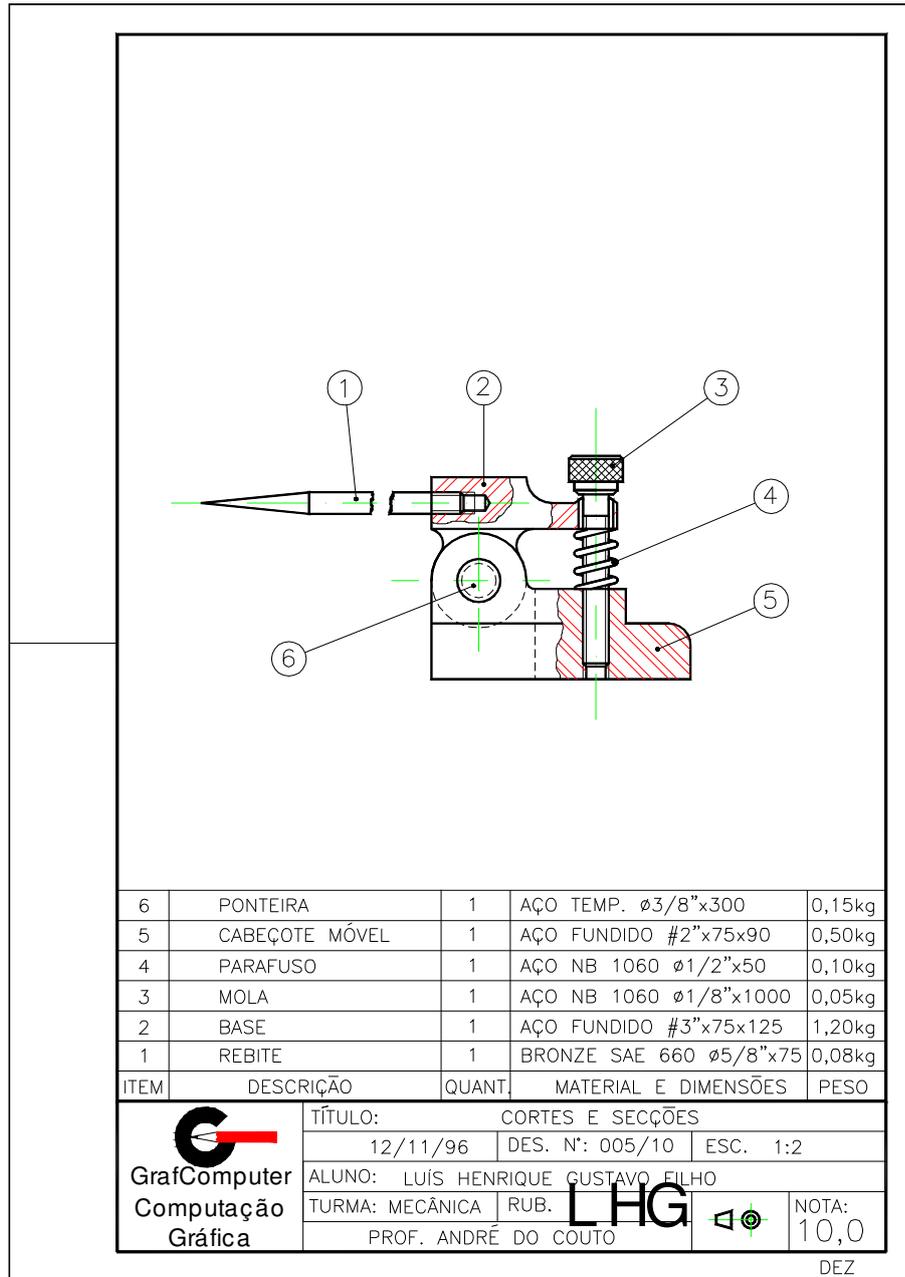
desenho de conjunto com designação das peças e lista de materiais.
